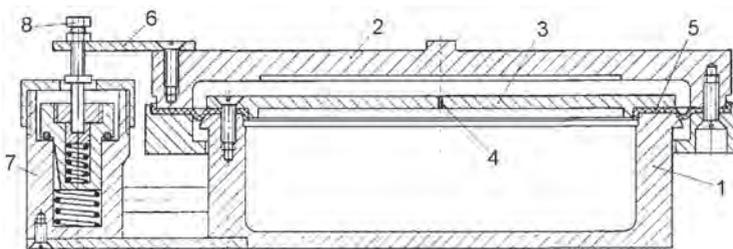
Конструктивная схема пневматической виброизолирующей системы: 1–корпус; 2–крышка; 3–перегородка; 4–межкамерный дроссель; 5–эластичная диафрагма; 6–рычаг обратной связи; 7– автоматический регулятор уровня; 8–регулирующий винт.
